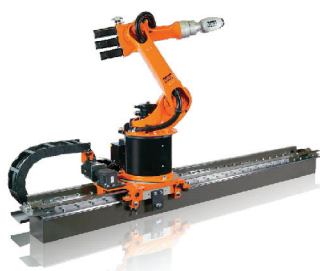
Фрезерный роботизированный комплекс Kuka на линейном блоке
